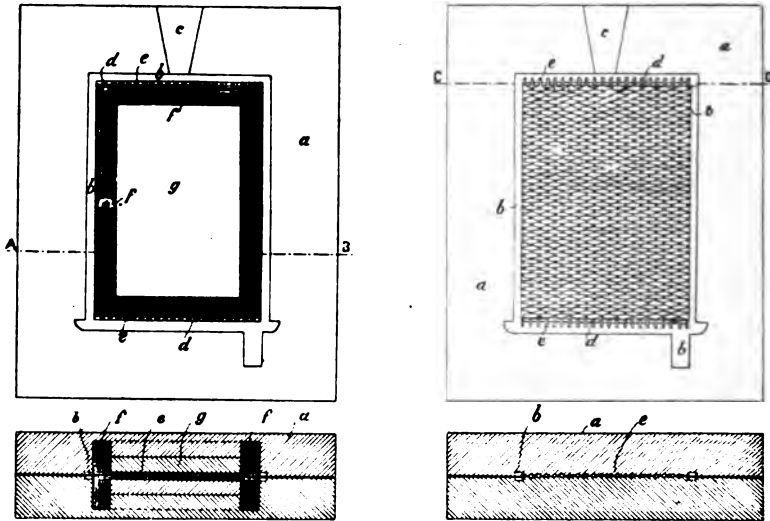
, 391, 392 et 393. — Moule Gölcher.
